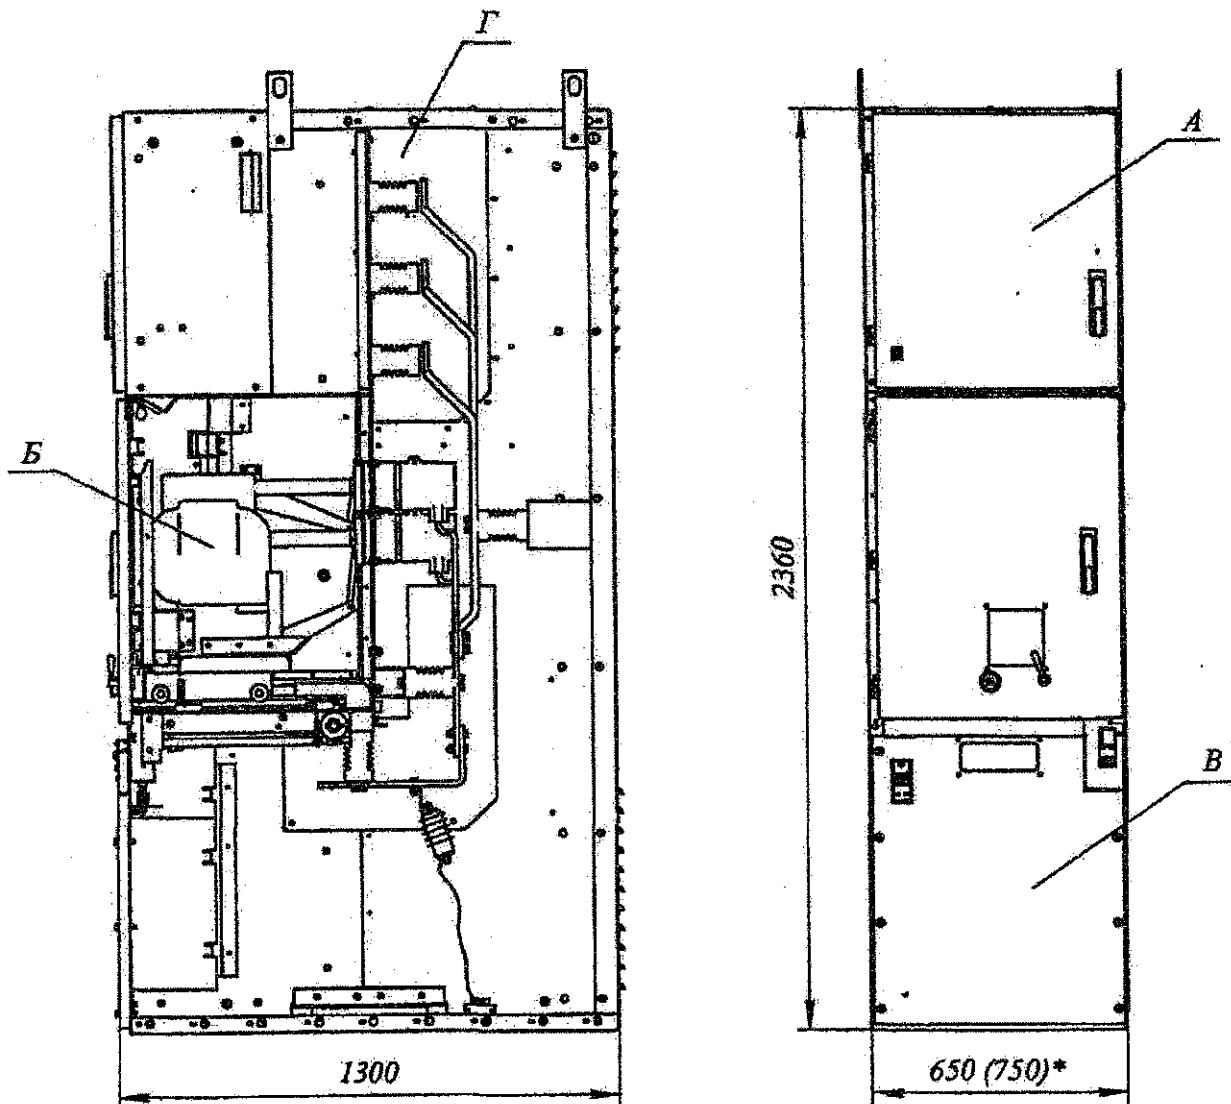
Общий вид и габаритные размеры шкафа КС-10 с трансформатором собственных нужд (ШСТ)
